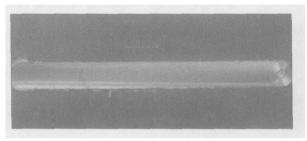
成形良好的焊缝 Fig 3 Well shaped well
